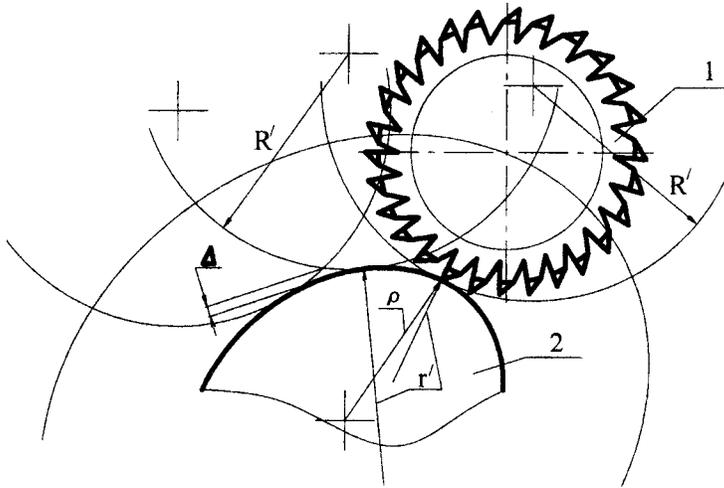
Схема образования огранки на поверхности профильного вала дисковой фрезой:
